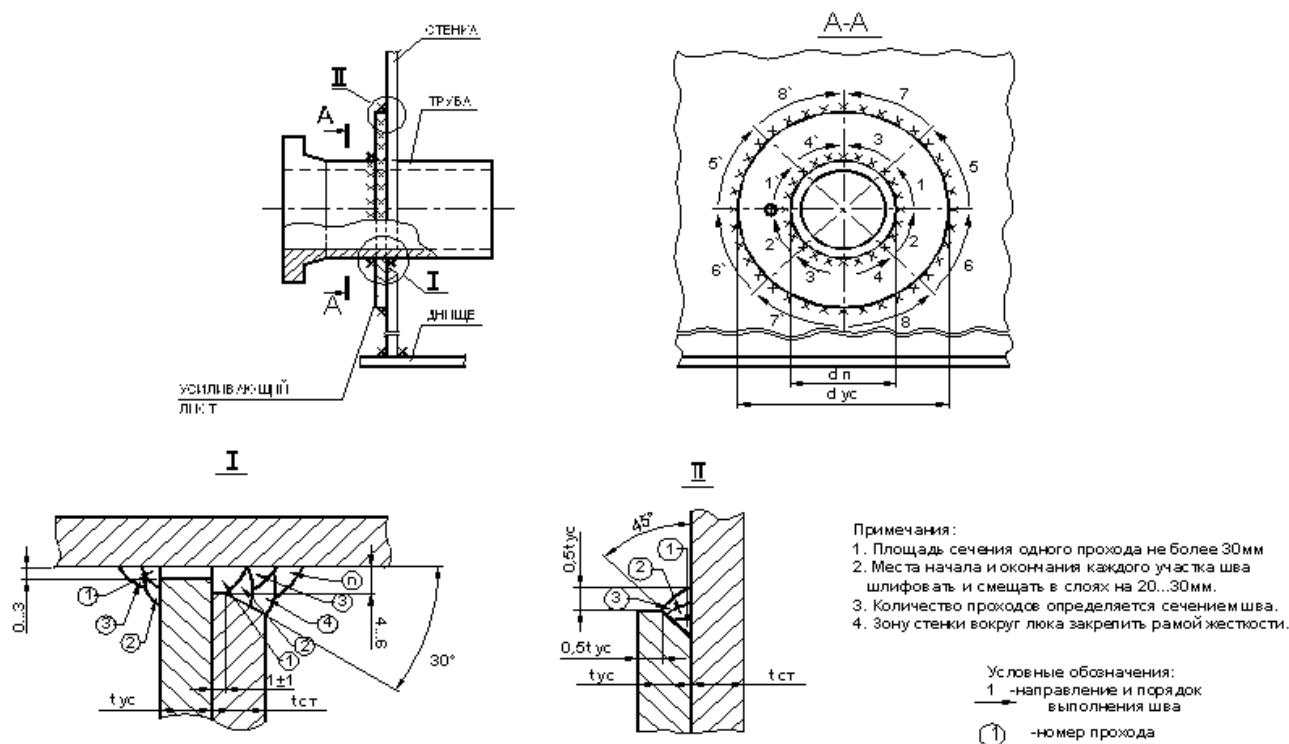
Схема сварки патрубков в стенке с усиливающим листом
